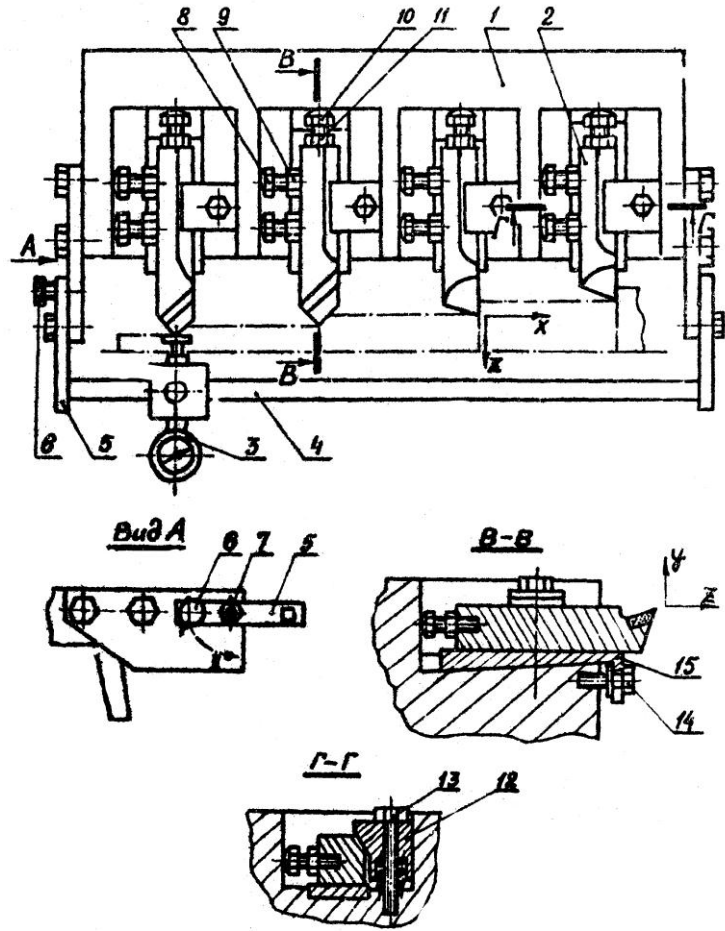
Блок резцов: 1 – корпус; 2 – резец; 3 – индикатор; 4 – направляющая; 5 – планка; 6- винт фиксации планки; 7 – ось планки; 8, 9 – установочные винт и контргайка/ось x/; 10, 11 – установочные винт и контргайка (ось z); 12 – прижим; 13 – винт; 14 – винт; 15 – клин
